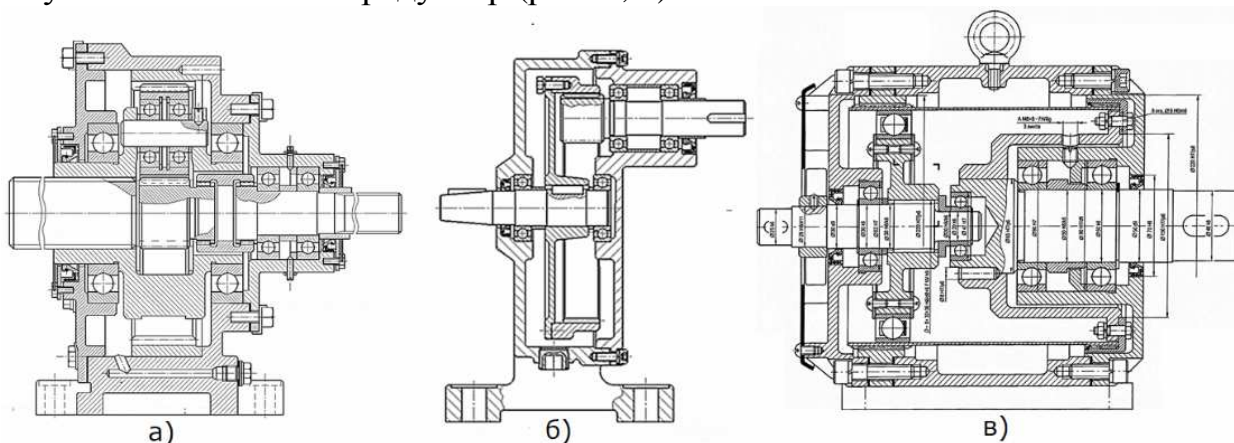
Планетарная (а) простая (б) схемы редуктора с внутренним зацеплением и схема волнового (в) редуктора
